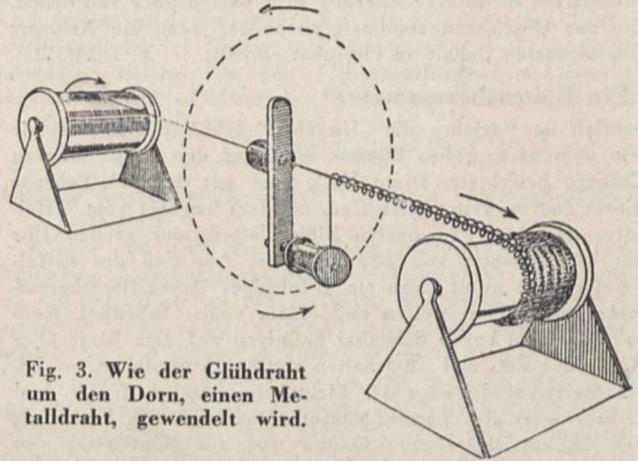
Wie der Glühlampendraht um den Dorn, einen Metalldraht, gewickelt wird.
